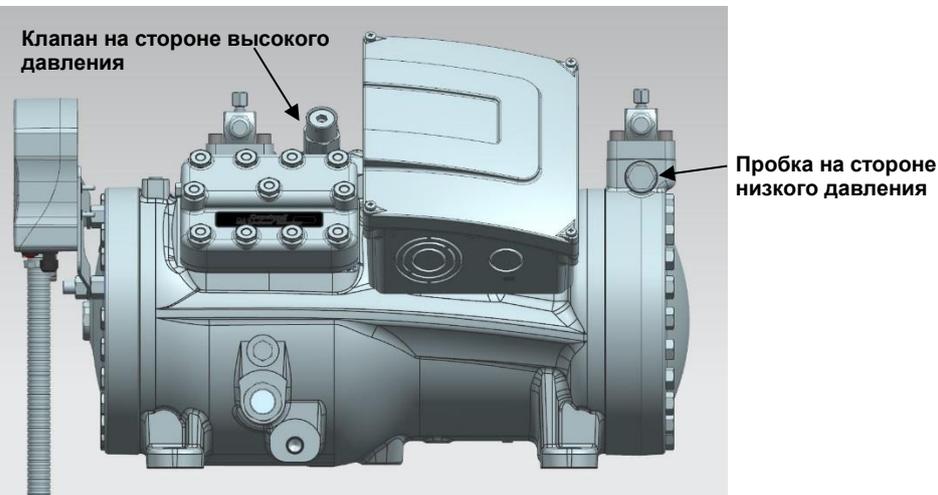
Расположение предохранительного клапана на компрессорах 4MTL05/07/09 и 4MSL03/04/06
